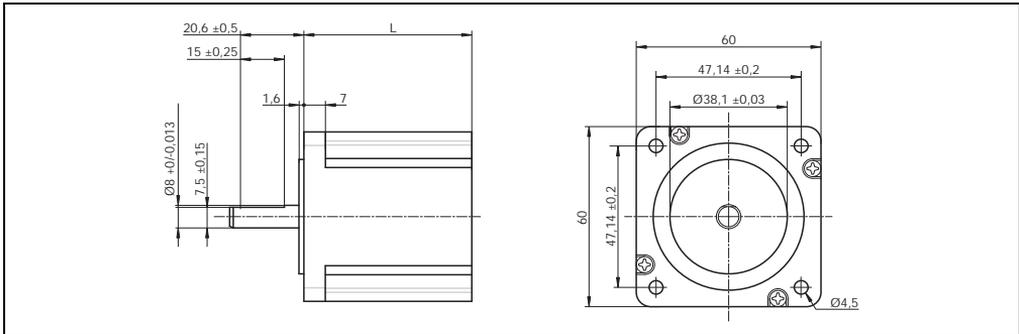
Schrittmotoren Flanschmaß 60 mm - Mechanische Abmessungen
